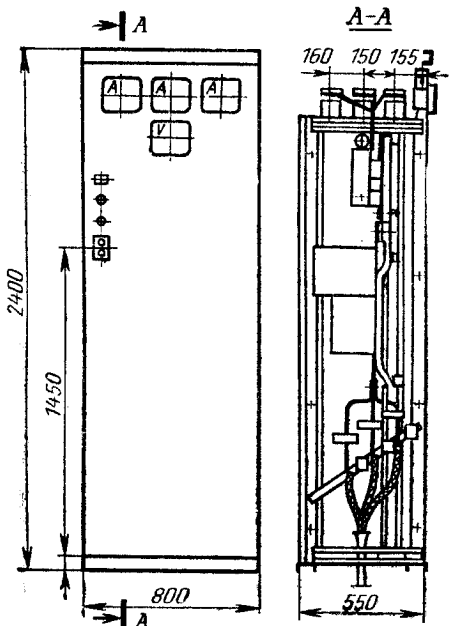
Общий вид и габаритные размеры панелей ПРС-I.
